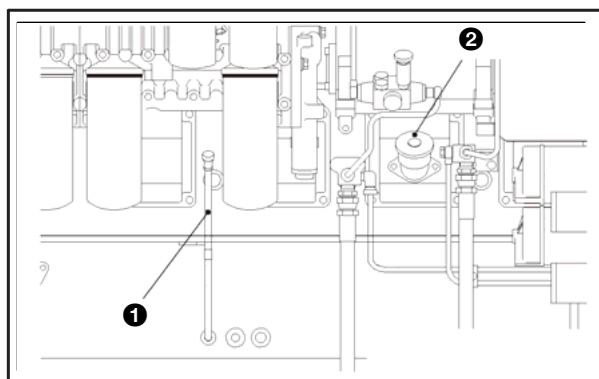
Empaquetadura de la cabeza de la bomba de cebado
